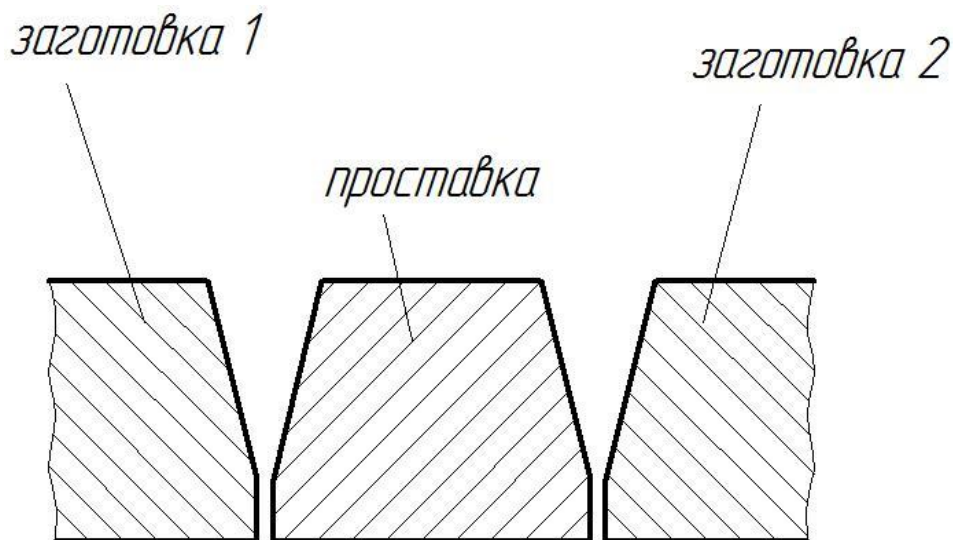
Сварка с использованием промежуточной проставки согласно [1]
